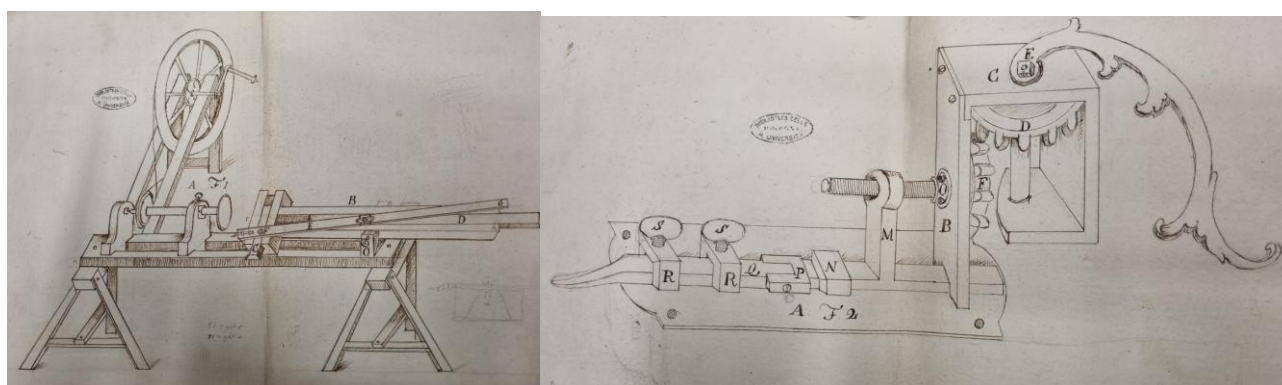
Macchina di Giuseppe Bruni, dettagli
